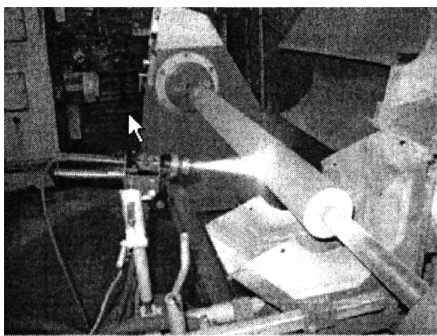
Шток-компрессора ОАО «Нафтан» – покрытие «Черный корунд»
